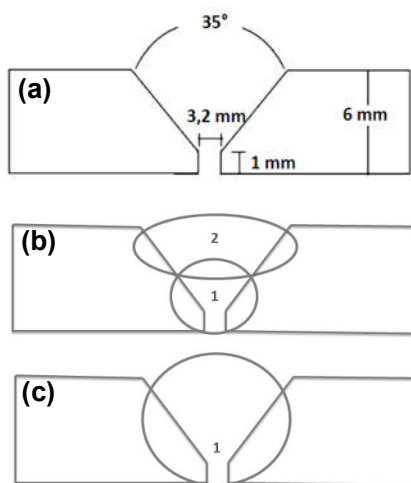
Esquema de soldagem passe de raiz, método dupla-fusão pelo processo GTAW
